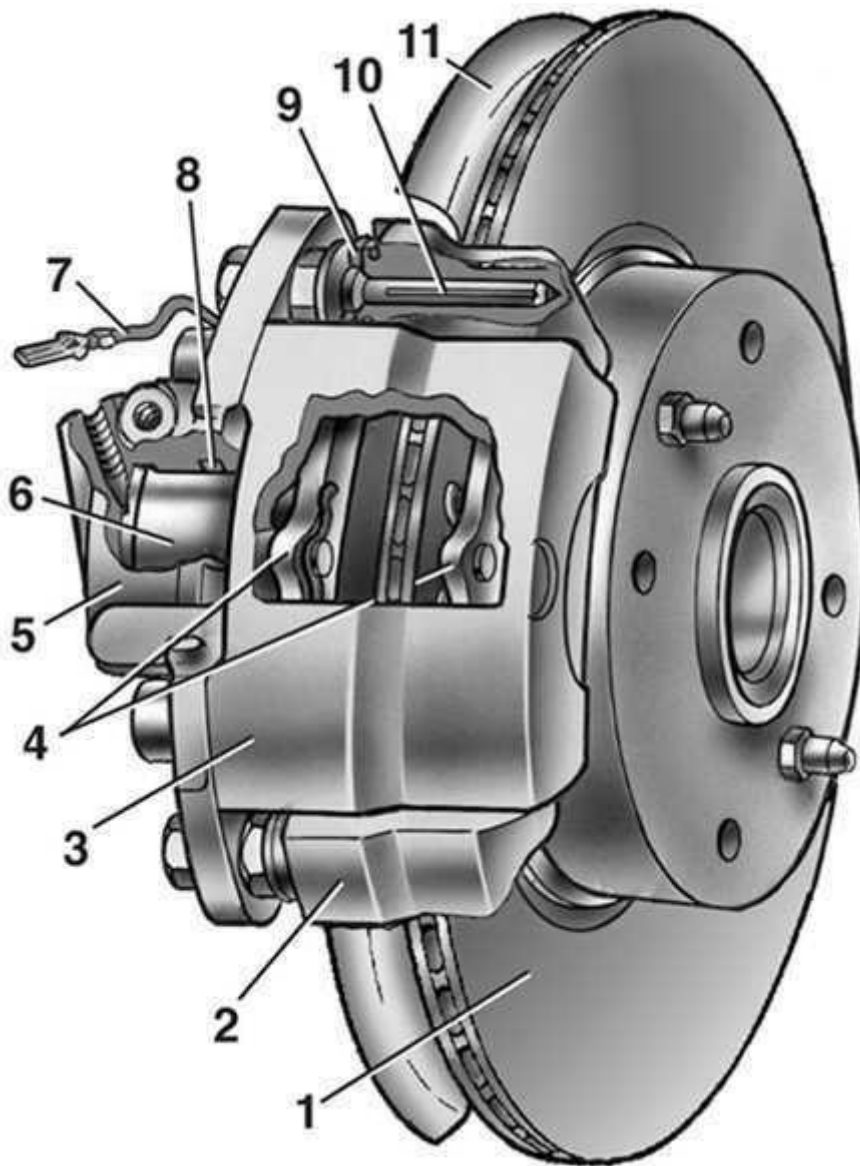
Дисковый тормозной механизм с плавающей скобой:
